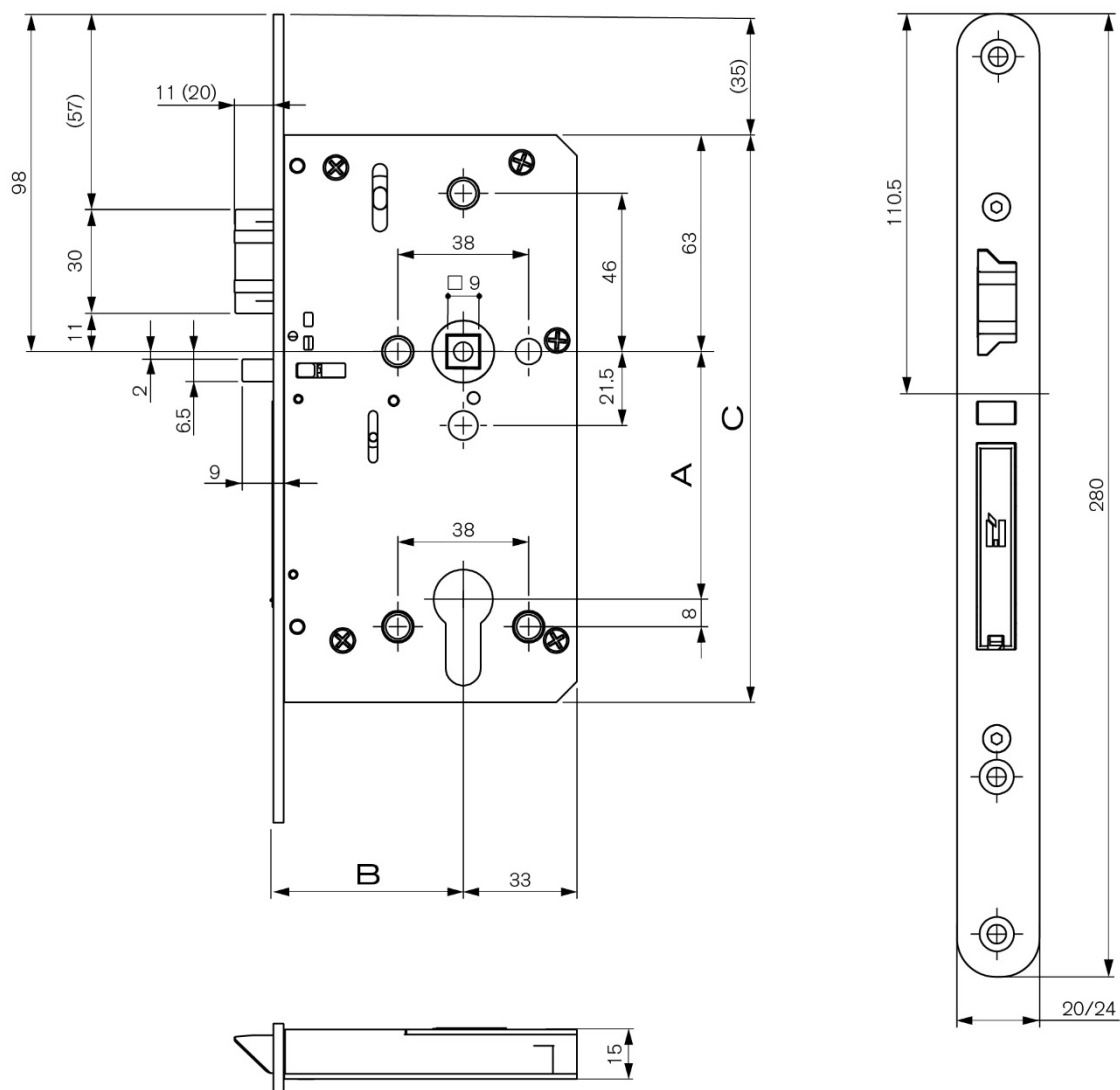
Abmessungen für Schlossinstallation – Profilzylinder 92
